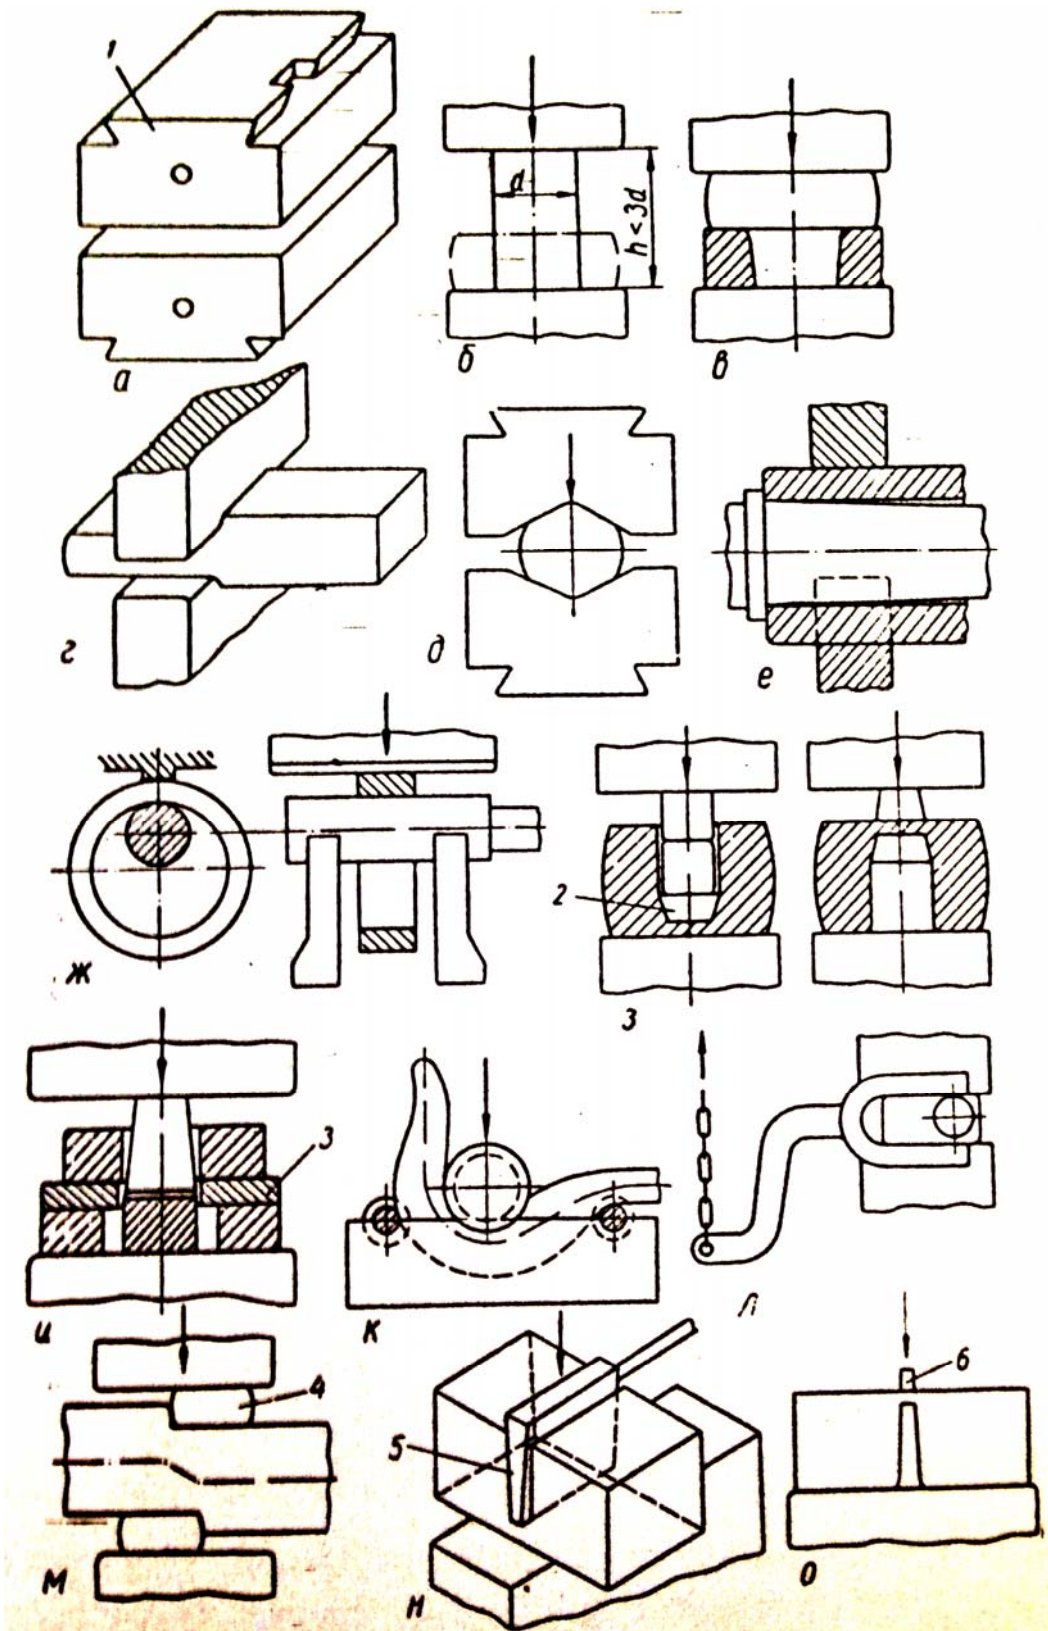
Схеми виконання основних операцій вільної ковки: а - бойки; б - осадка; в - висадка; г - витягання плоскими бойками; д- витягання фасонними бойками; г - витягання за допомогою оправки; ж - роздача на оправці; з - прошивка; і - прошивка на підкладном кільці; к - гнучка; л - закручування; м - передача; н - рубка; о - закінчення рубки відсіченням.
